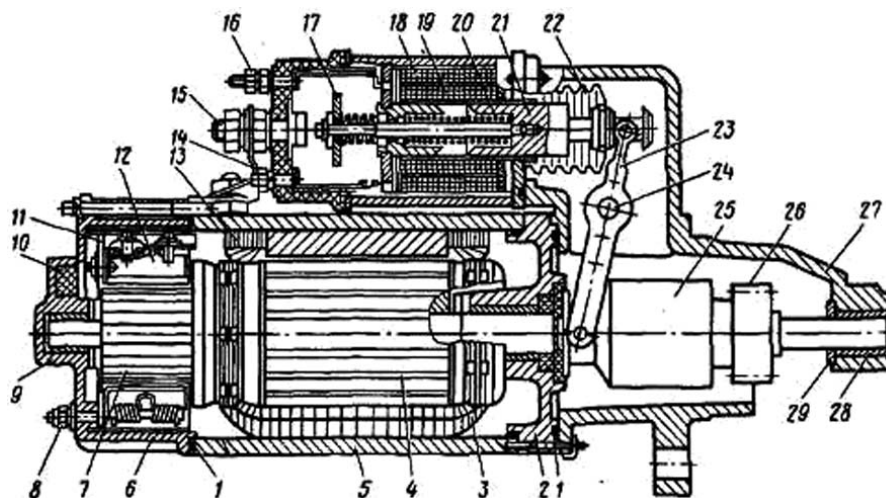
Стартер СТ142Б: 1 — уплотнительные кольца; 2 — держатель промежуточного подшипника; 3 — бандаж; 4 — якорь; 5 — корпус; 6, 27 — крышки; 7 — коллектор; 8 — болт крепления траверсы щеткодержателей; 9, 28 — по дшипник; 10 — фольга; 11 — траверса щеткодержателей; 12 — щетки; 13 — обмотка возбуждения; 14 — соединительная шина; 15 — основной зажим; 16 — зажим обмоток реле; 17 — контактный диск; 18, 19 — втягивающая и удерживающая обмотки; 20 — возвратная пружина; 21 — якорь; 22 — резиновый кожух; 23 — рычаг привода; 24 — эксцентриковая ось; 25 — привод; 26 — шестерня; 29 — упорная шайба
